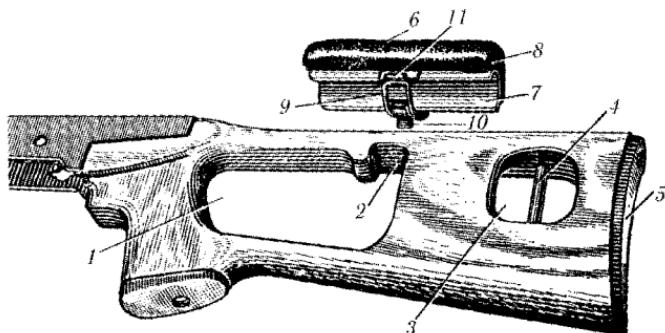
Приклад СВД-63 со щекой: 1 — вырез, образующий рукоятку; 2 — вырез для застежки замка щеки приклада; 3 — окно; 4 — антабка; 5 — металлический затыльник; 6 — щека; 7 — деревянное основание; 8 — мягкая набивка; 9 — петля; 10 — застежка; 11 — зацеп обоймы.
